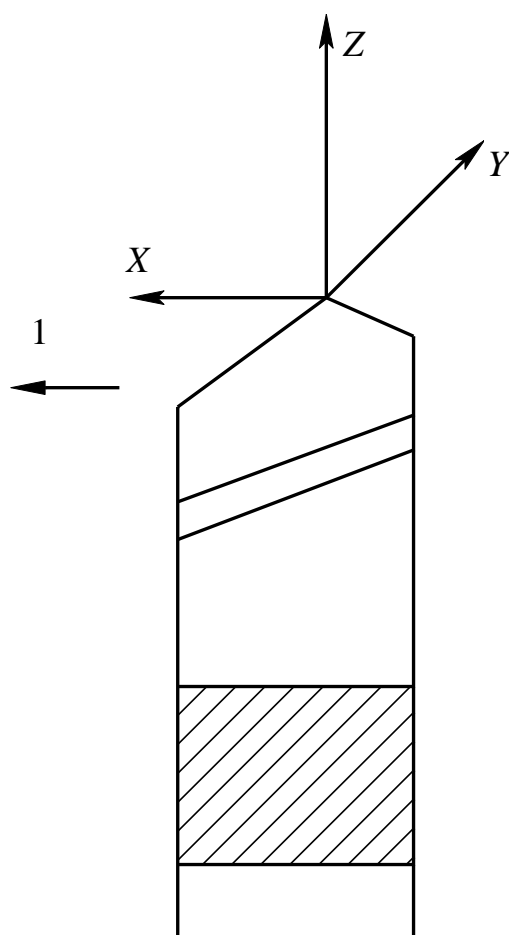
Собственная система координат токарного резца с державкой прямоугольного сечения
